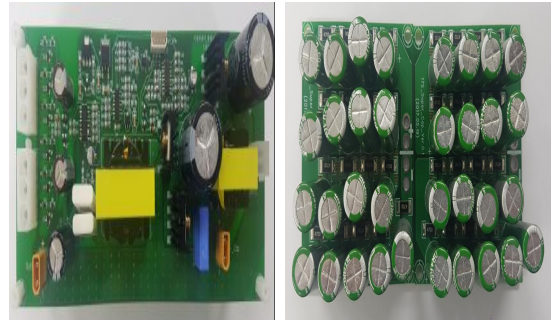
제안 부스트 컨버터 시작품 PBA 및 Super Cap. String
